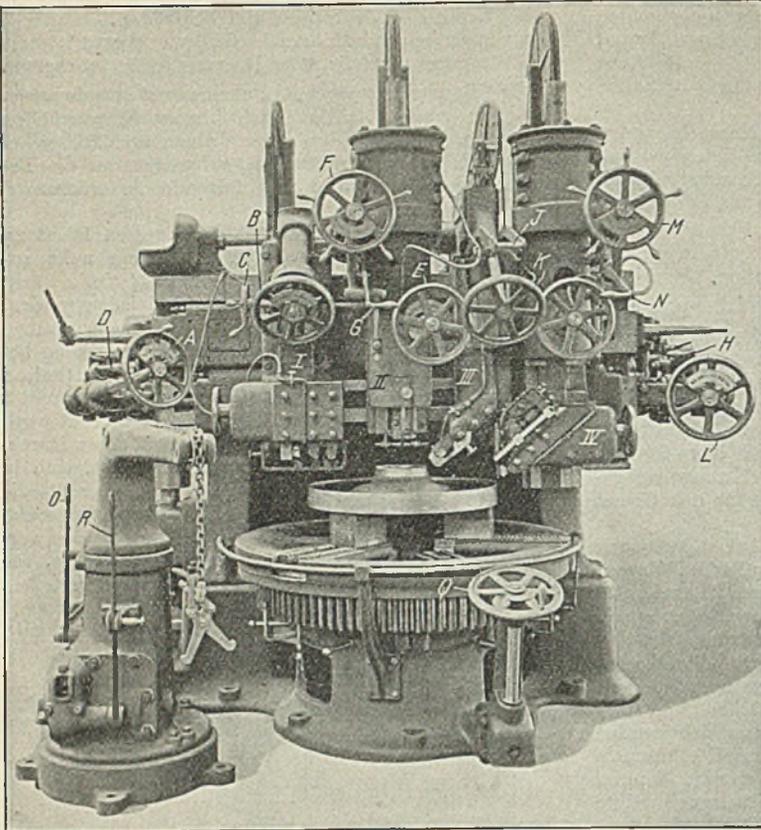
Spezialmaschine zum Bearbeiten von Radkörpern.
